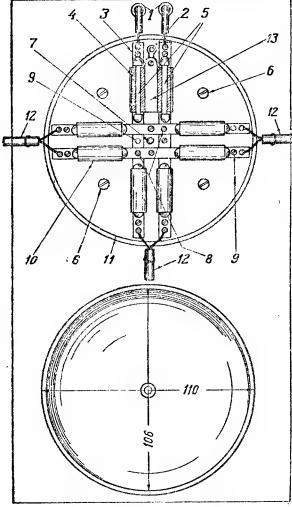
Устройство коробки: 1—вводные втулки; 2—отверстие для заземления; 3—металлические пластинки для крепления проводов; 4— угольные пластинки; 5—предохранители; 6— шурупы, крепящие коробку к стене; 7— болт для крепления крышки коробки; 8—болты, крепящие шины коробки; 9—болты, крепящие шины коробки; 10—емкостные ограничители; 11—вырез для краев крышки коробки; 12—ответвления к абонентам; 13—металлическая пластинка для заземления
